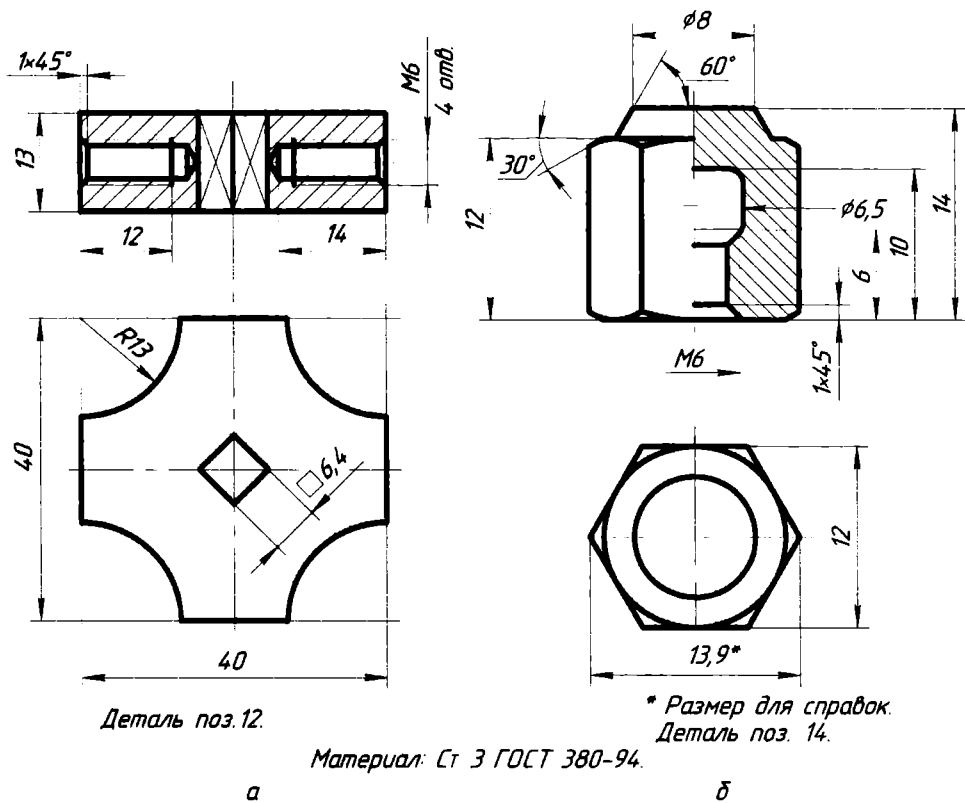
Чертежи: а — крестовины; б — гайки
